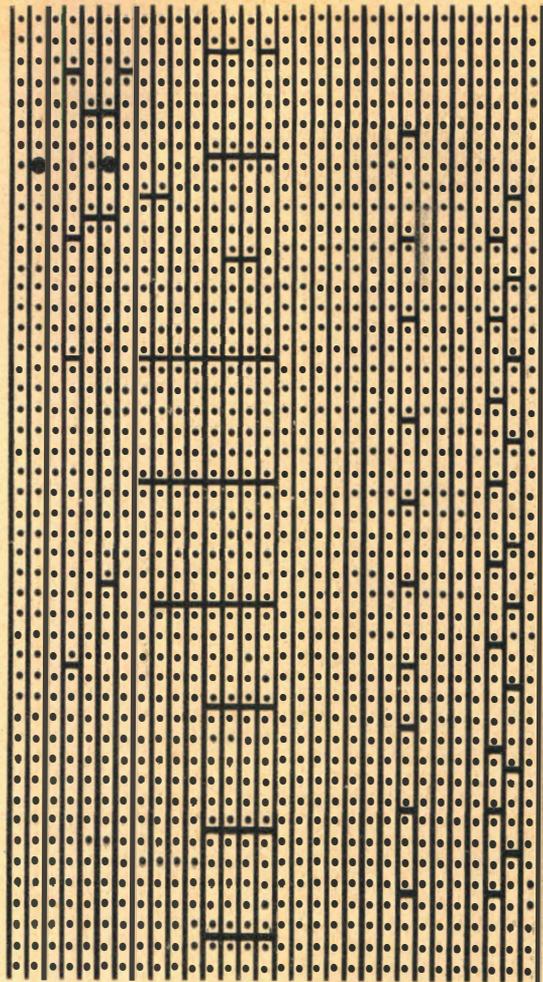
Plaqueta de circuito impresso universal, vista pela face cobreada, mostrando as interrupções necessárias.
